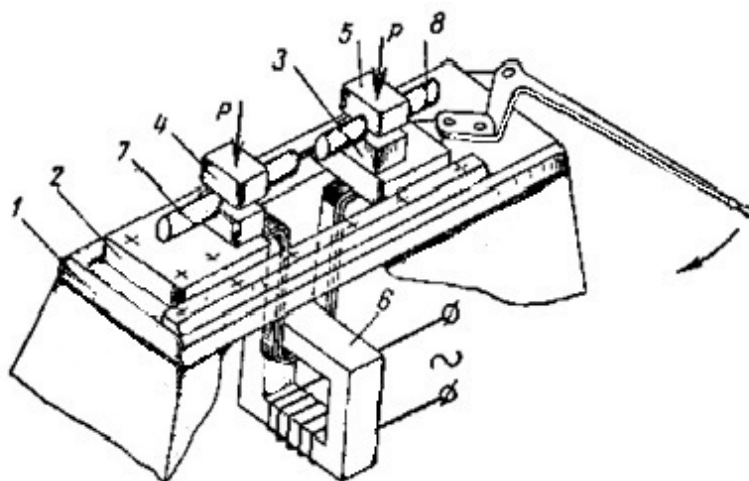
Схема машины для стыковой контактной сварки
